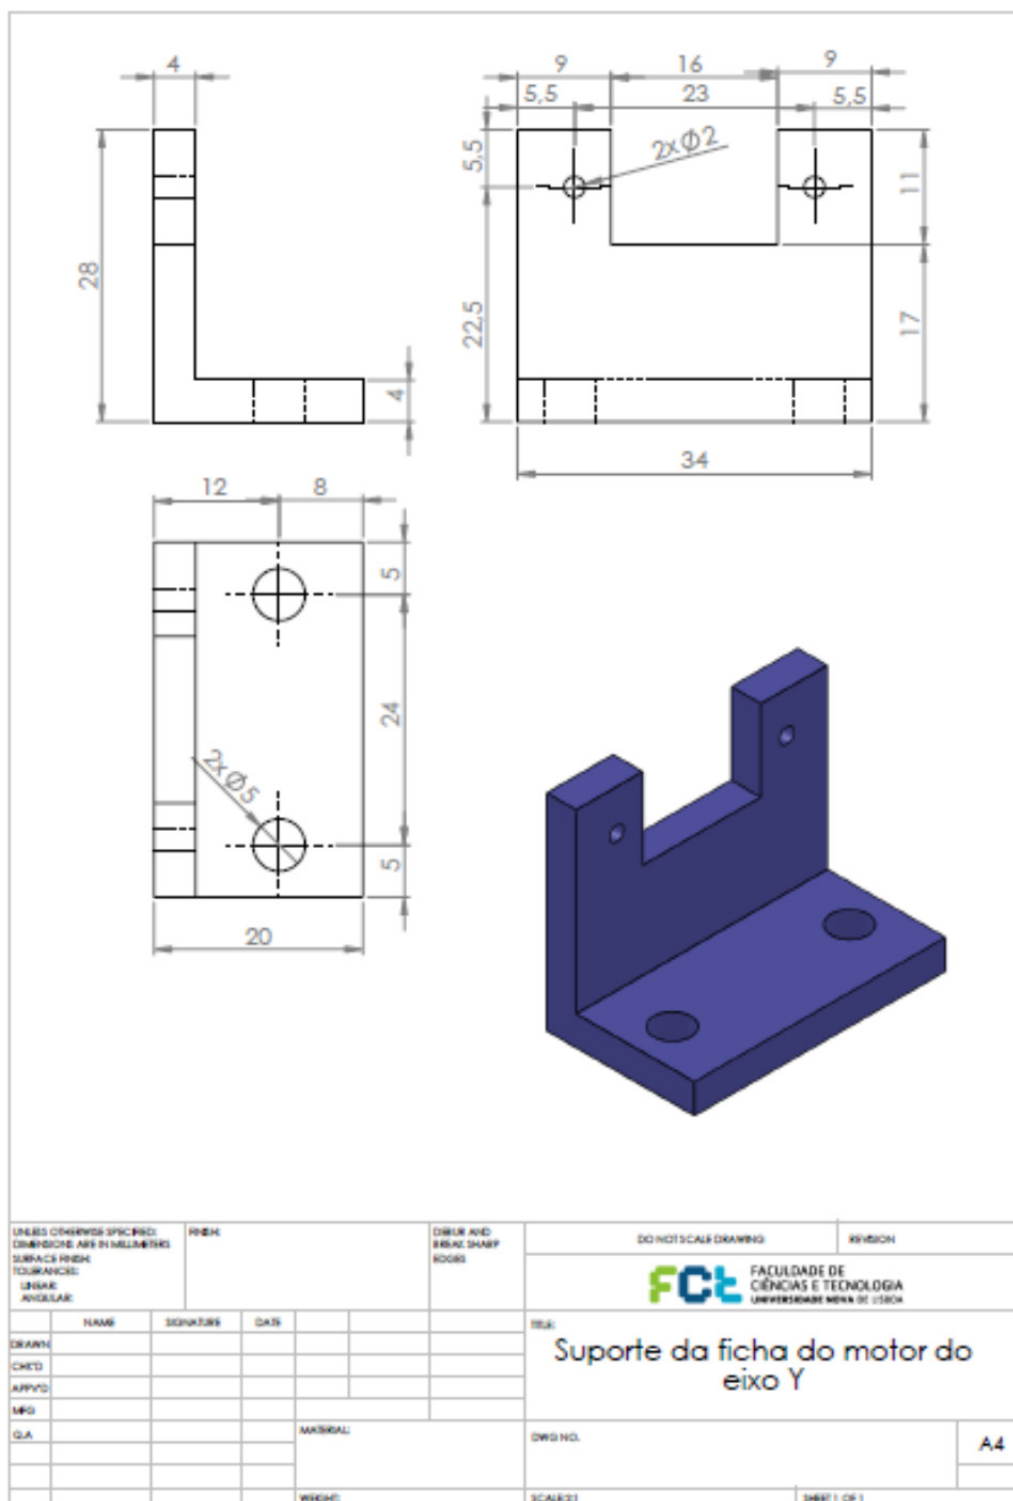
Desenho técnico do suporte da ficha para o motor do eixo Y
